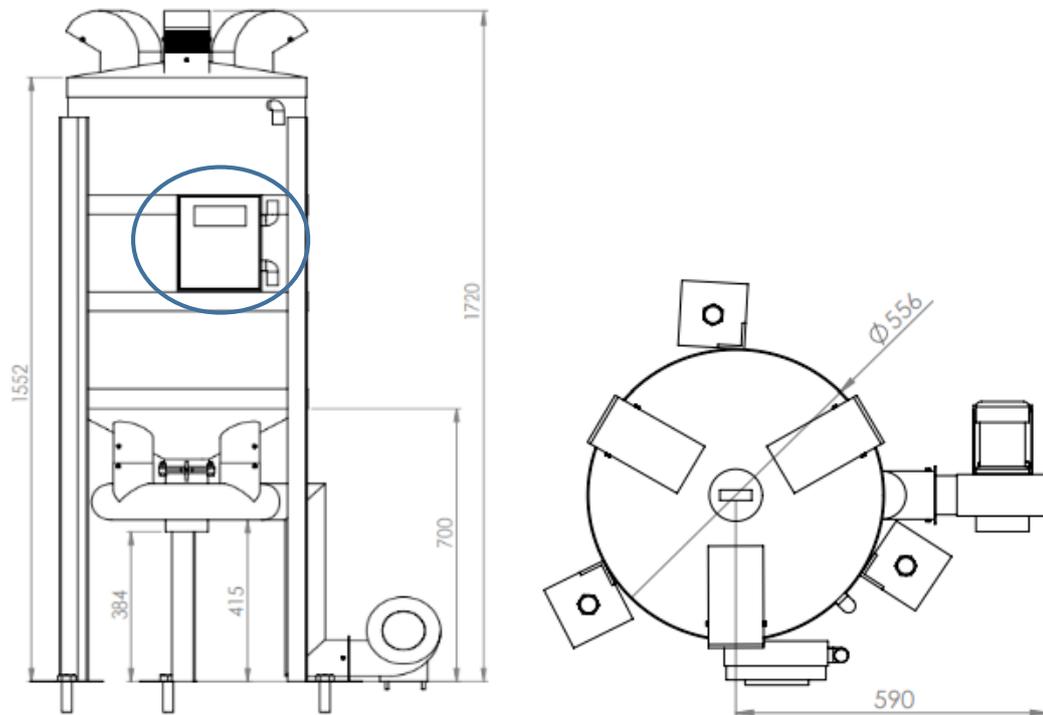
Vista frontal y superior acotada en mm del sistema de almacenamiento
